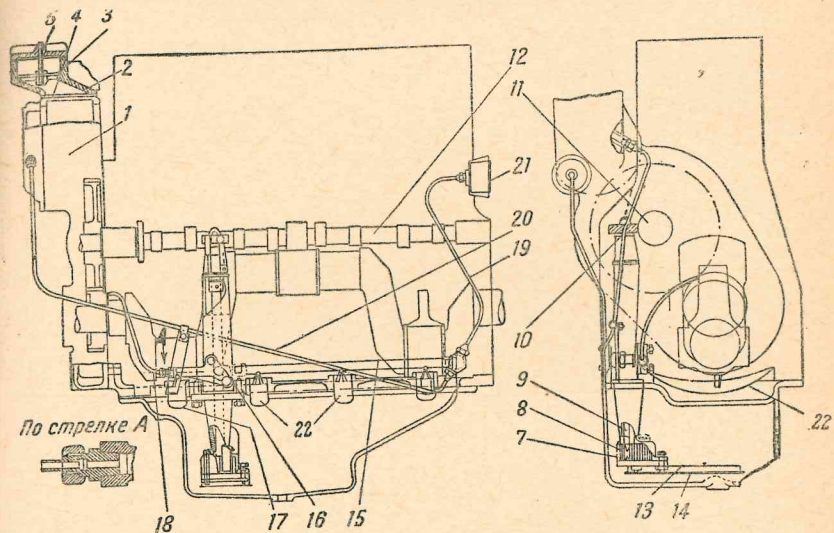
Схема смазки двигателя СТЗ—ХТЗ
